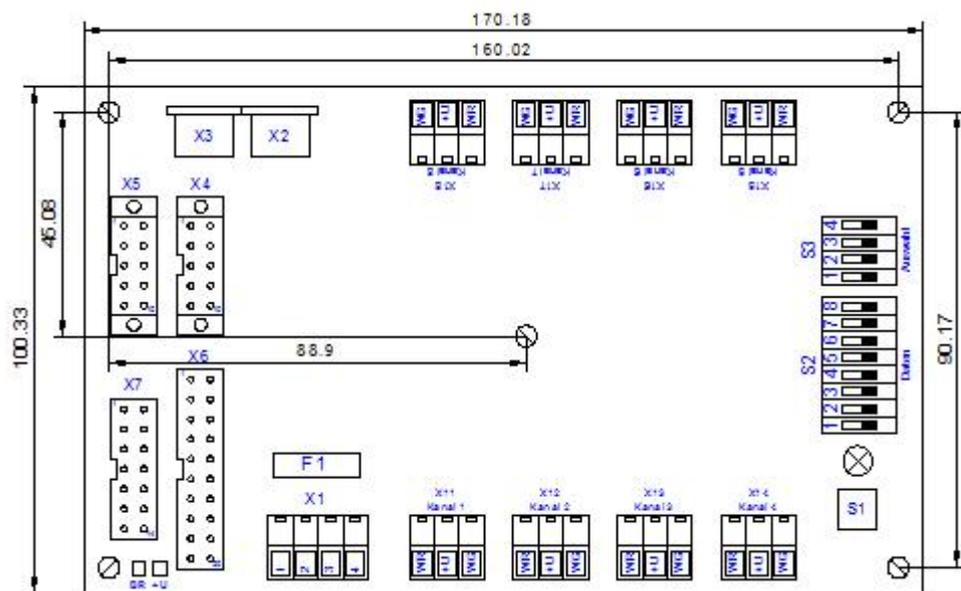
Lage der Anschlussstecker, Sicherung, Taster und das Befestigungslochbild
